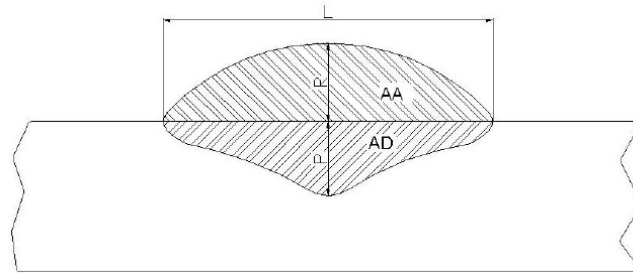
Representação esquemática das dimensões geométricas das seções transversais dos cordões de solda.
